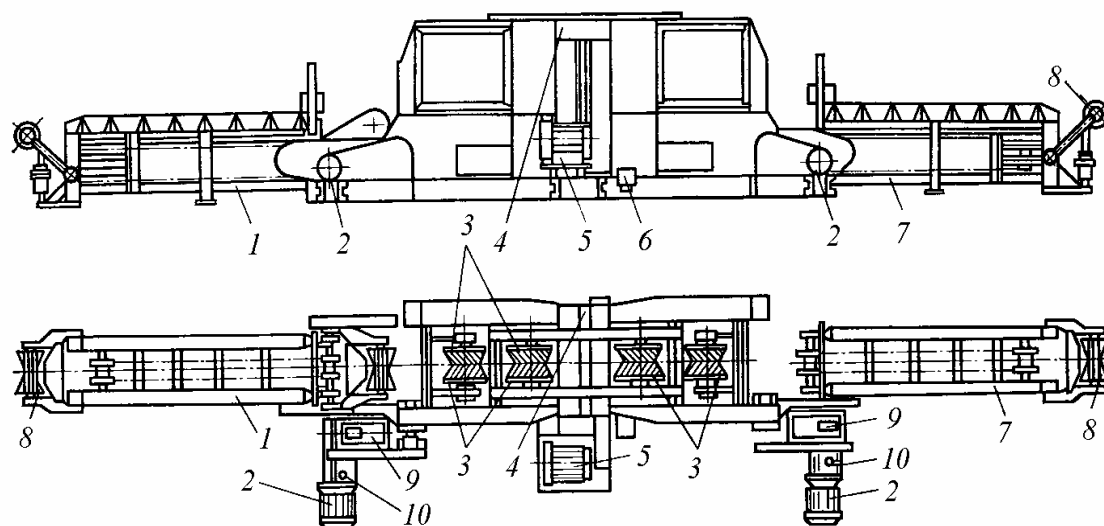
Схема роторных окорочных станков ОК40-1, ОК63-1 и ОК80-1:
